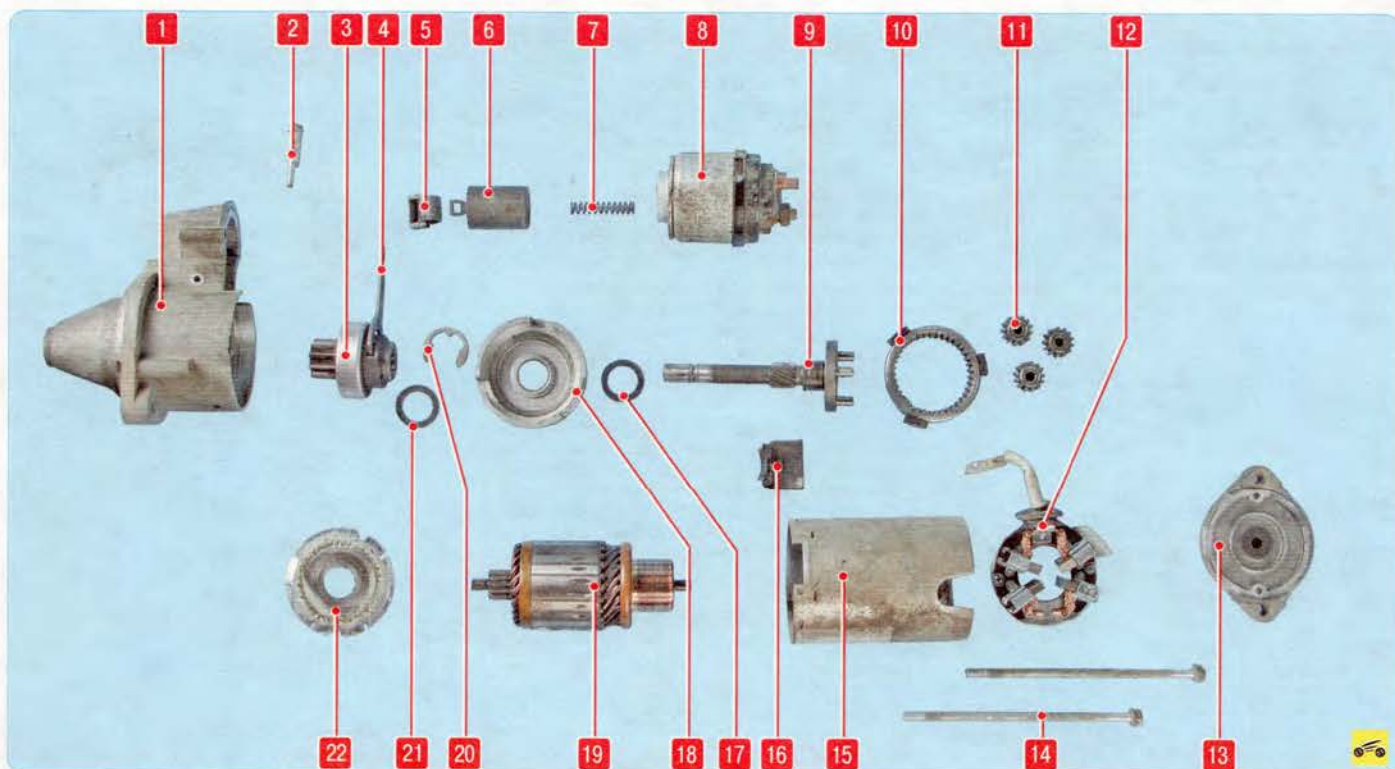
Детали стартера 6012.3708: 1 – передняя крышка стартера; 2 – ось рычага; 3 – обгонная муфта; 4 – рычаг привода обгонной муфты; 5, 16 – резиновые уплотнения; 6 – якорь тягового реле; 7 – пружина якоря реле; 8 – корпус тягового реле; 9 – вал привода; 10 – коронная шестерня планетарного редуктора; 11 – шестерни-сателлиты планетарного редуктора; 12 – щеточный узел; 13 – задняя крышка стартера; 14 – стяжные болты; 15 – корпус статора; 17, 21 – кольца; 18 – корпус планетарного редуктора; 19 – ротор; 20 – стопорное кольцо; 22 – крышка редуктора стартера
